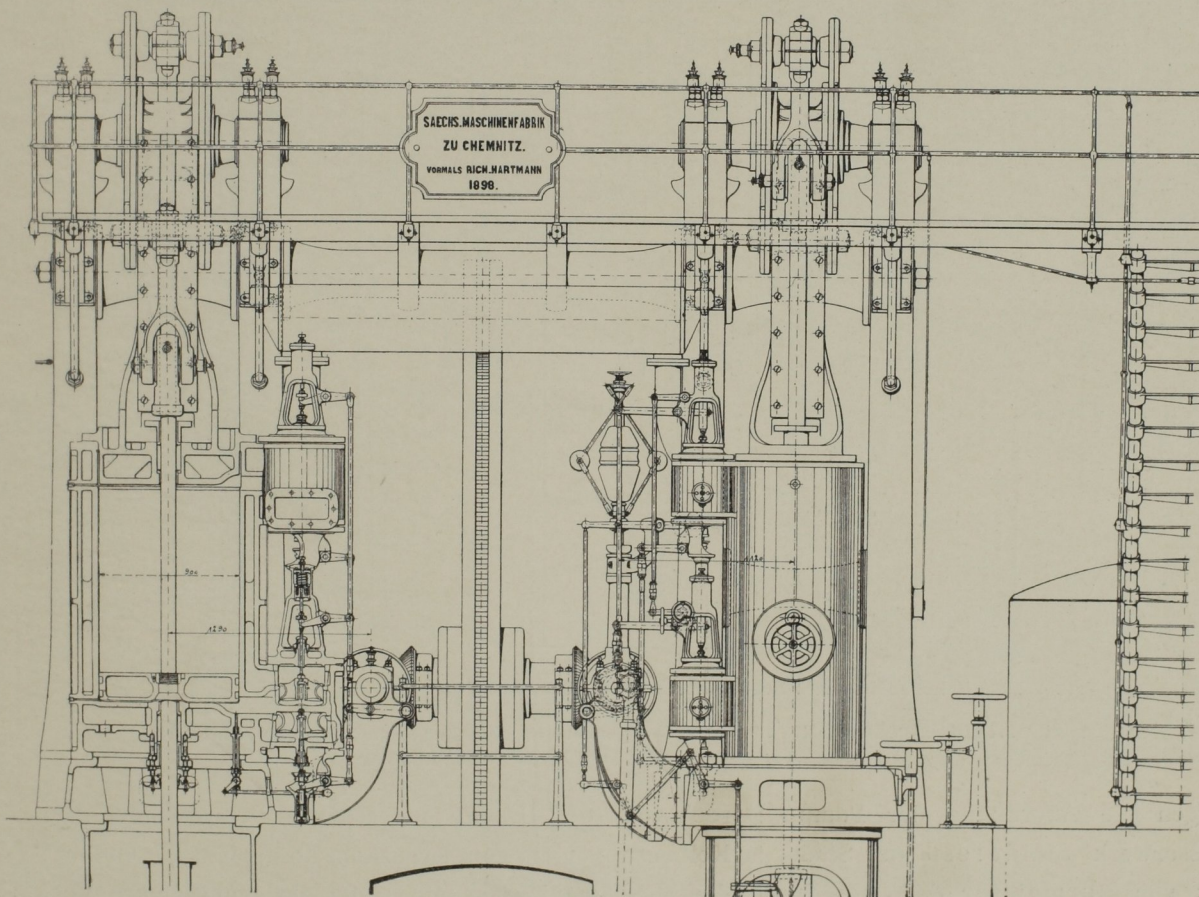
Seitenansicht und Schnitt der Dampfmaschine. Massst. 1:45.
